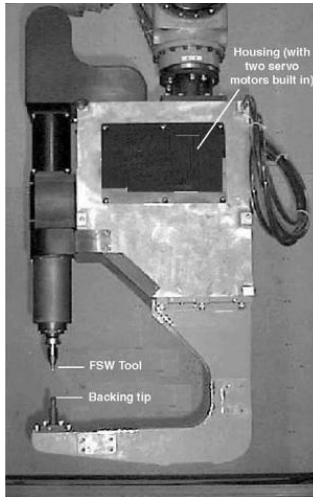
Dispositif de soudage FSSW (SMY+01)
